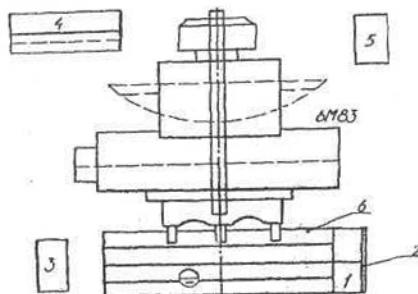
Примерная схема рабочего места станочника: 1 – инструментальная тумбочка; 2 – кронштейн для подвешивания чертежей; 3 – приемный столик; 4 – стеллаж для приспособлений; 5 – стойка-стеллаж; 6 – решетка для ног
